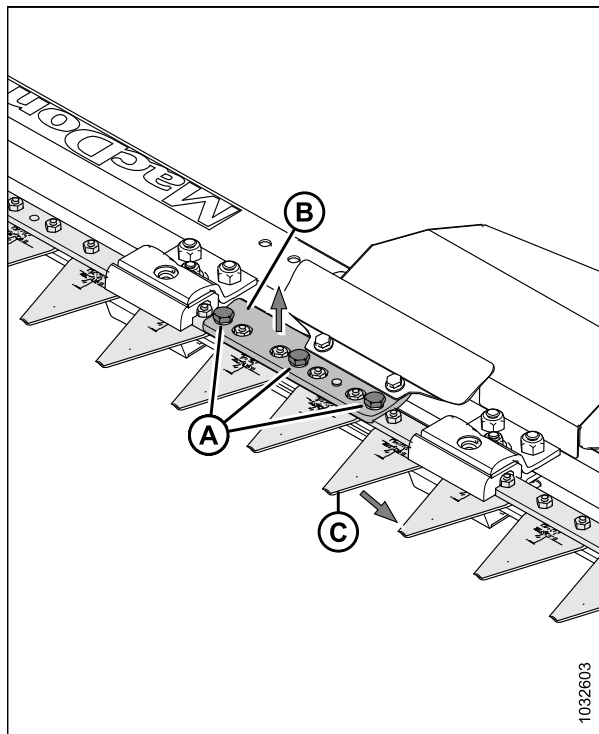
Вертикальный нож — противорежущий палец снят
